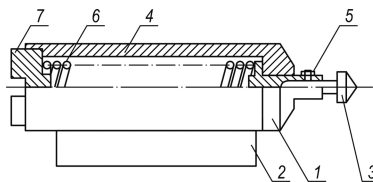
Приспособление для нанесения регулярного микрорельефа на боковую поверхность плунжеров топливных насосов высокого давления
